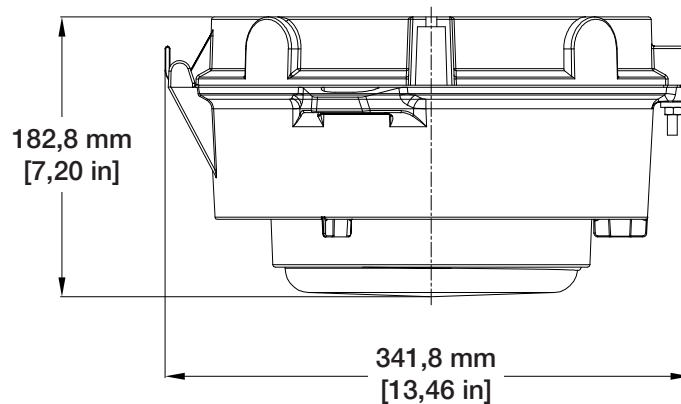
LUMINAIRE AVEC CAPOT DE PLAFOND
